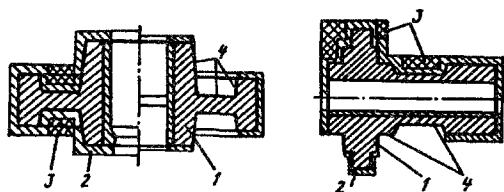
Соответствие формы детали и заготовки, полученной свободной ковкой и штамповкой в открытом штампе и на ГКМ; 1 — деталь; 2 — припуск; 3 — напуск; 4 — «исходные» поверхности детали
